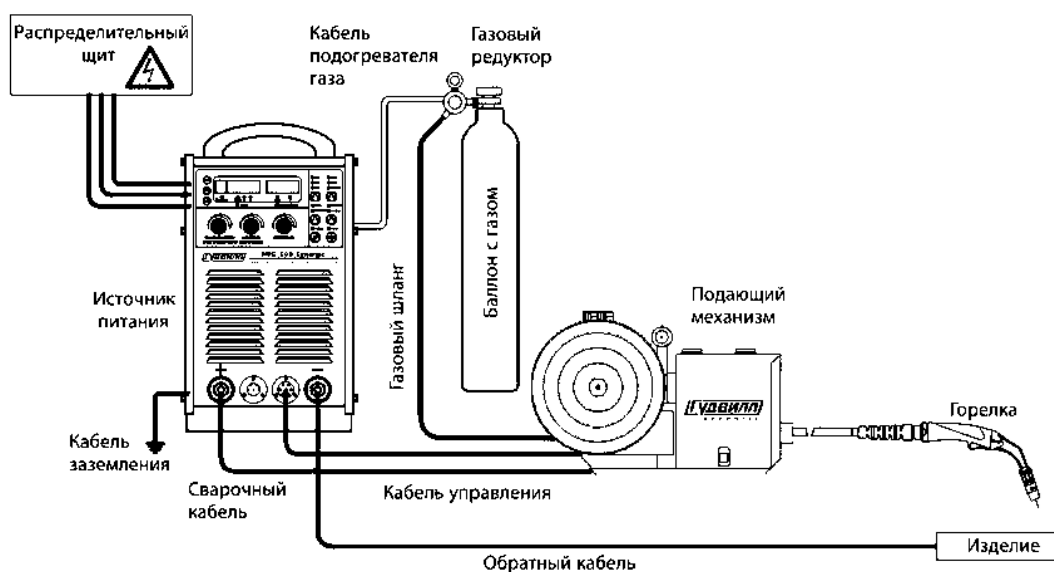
Схема установки для дуговой механизированной сварки в CO<sub>2</sub>
